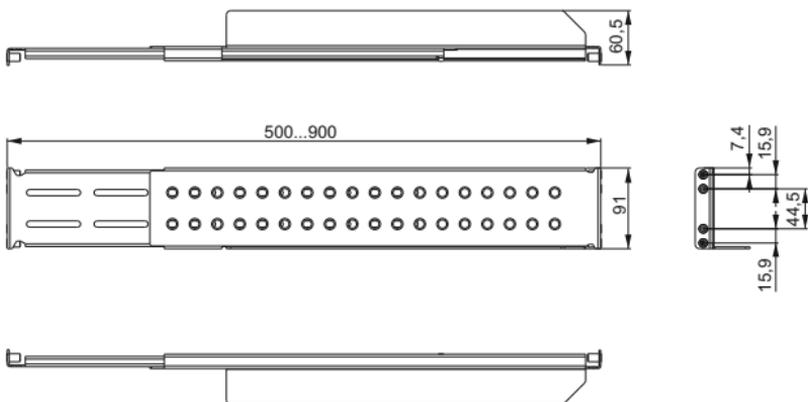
Габаритные и установочные размеры направляющих / Figure 1 – Overall and mounting dimensions of the guideways
